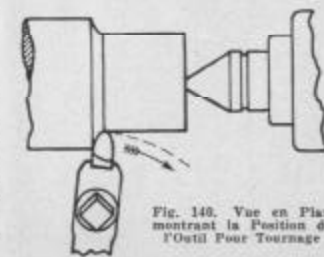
Vue en Plan montrant la Position de l'Outil Pour Tournage
